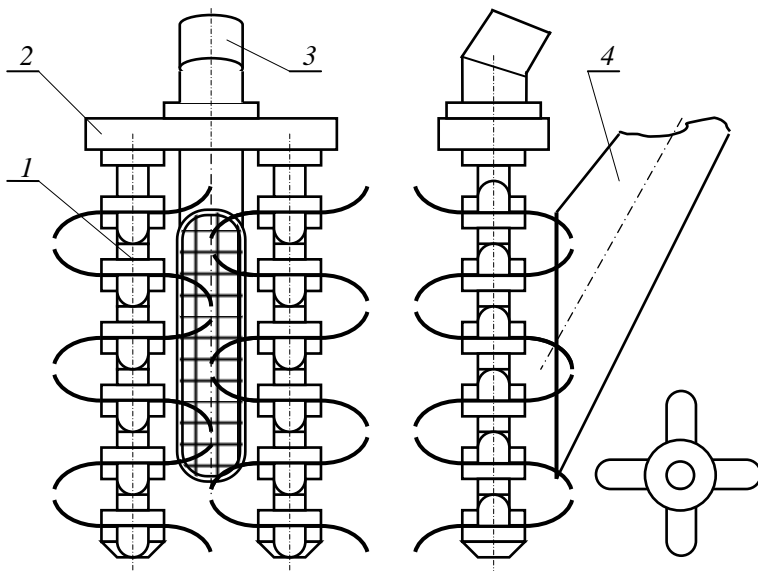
Схема двухфрезерного разрыхлителя.
